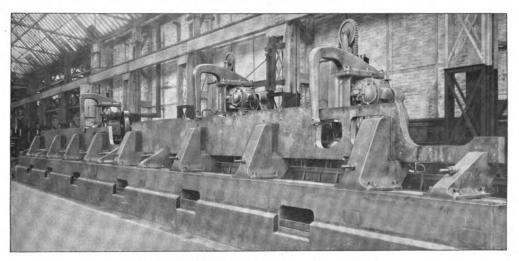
Dreiständrige Barrenrahmen-Fräsmaschine.
